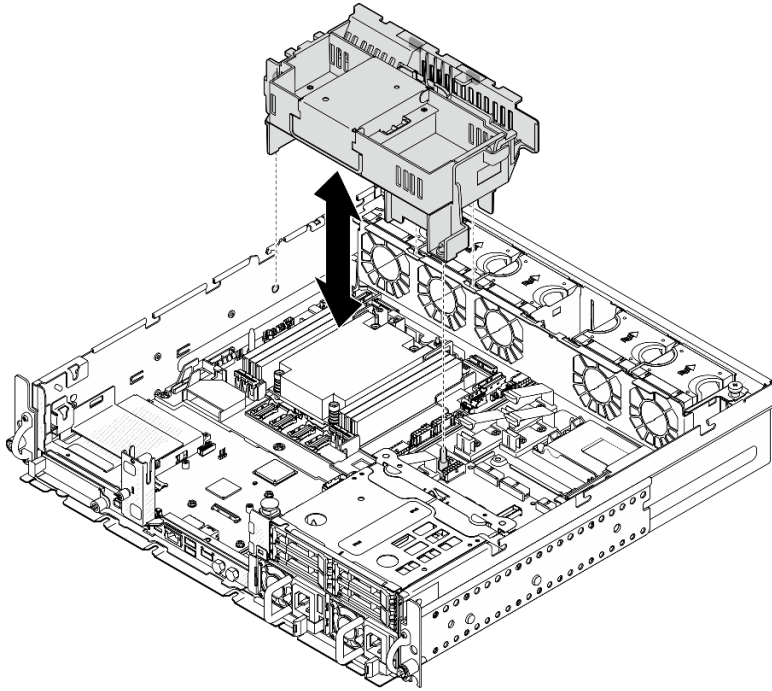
Installation de la grille d'aération pour dissipateur thermique 1U
